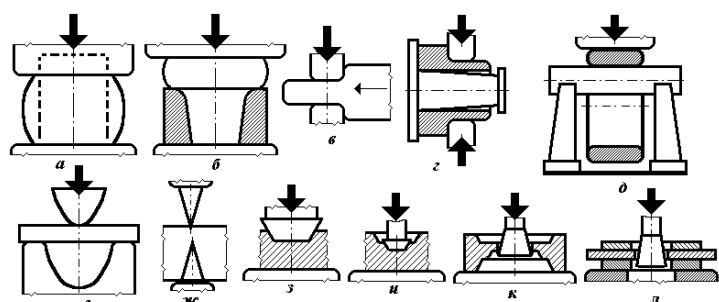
Основные операцииковки: а – осадка; б – высадка; в – протяжка; г – протяжка с оправкой; д – раскатка на оправке; е – гибка; ж – отрубка; з – прошивка неглубоких полостей; и – прошивка глубоких полостей; к – прошивка сквозных полостей; л - высадка с подкладкой; стрелками указаны направления действия силыковки
